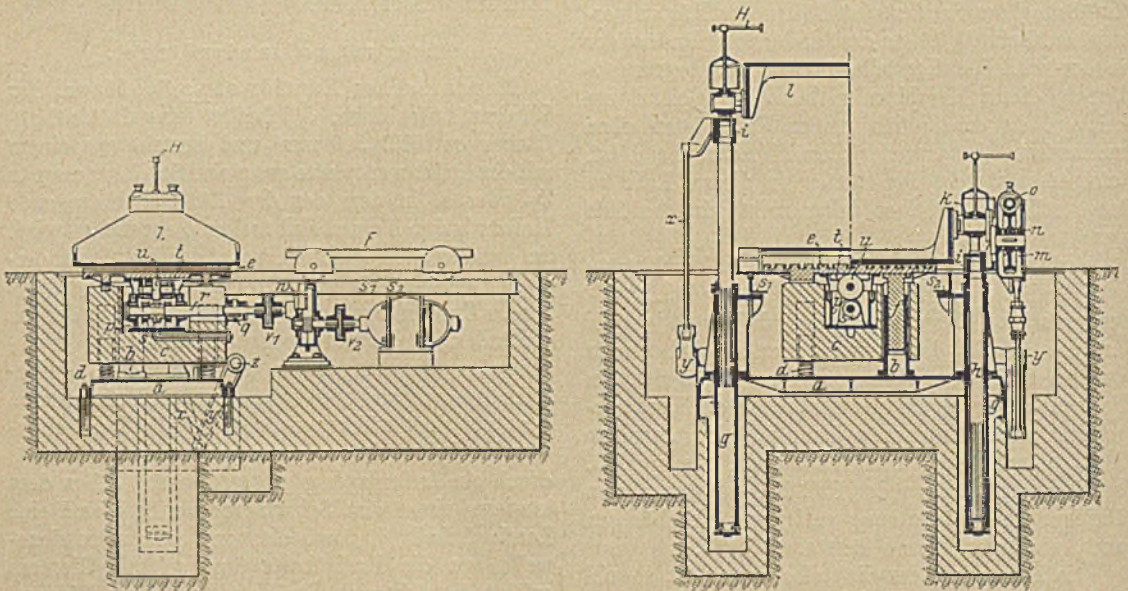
Elektrische Rüttelformmaschine mit Stoßfang, Wendepplatte, mechanischer Wende- und Druckwasser-Abhebevorrichtung.
